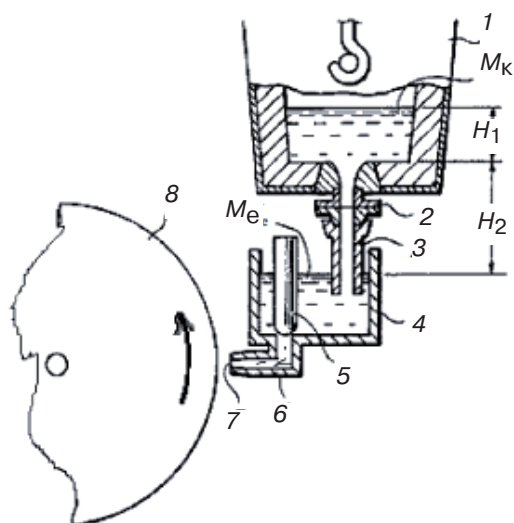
Схема подачи расплава сбоку через промежуточную емкость: 1 – разливочный ковш; 2 – шиберный затвор; 3 – стакан-дозатор; 4 – промежуточный ковш; 5 – стопор промежуточной емкости; 6 – разливочный насадок промежуточного ковша; 7 – сопло; 8 – барабан-холодильник; H_1 – высота (уровень) расплава в разливочном ковше; H_2 – столб расплава от основного разливочного ковша до уровня в промежуточном ковше; M_k и M_e – уровни металла в разливочном и промежуточных ковшах, соответственно
